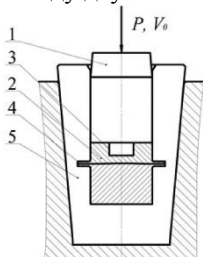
Схема изготовления биметаллического инструмента с формообразующей полостью
